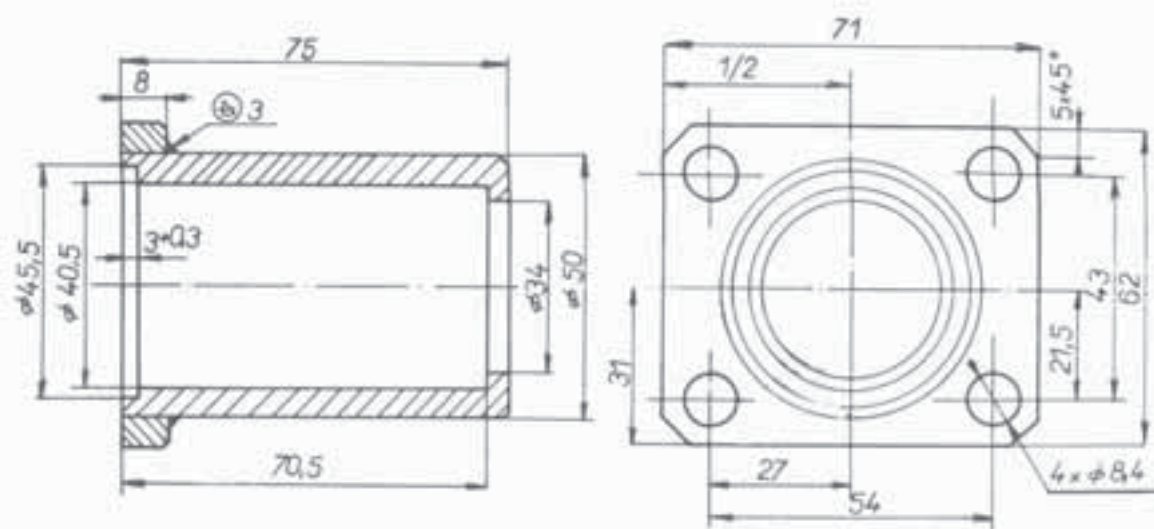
Приспособление для снятия нижнего уплотнительного кольца с золотника
